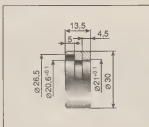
Направляющая втулка для запрессовки поршня в цилиндр.
